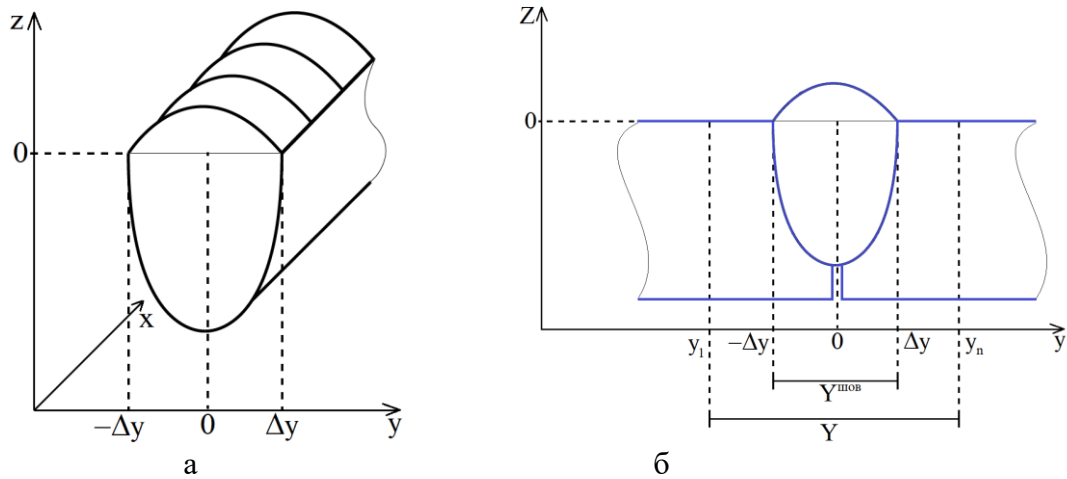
Принципиальный график (а) и поперечное сечение (б) сварного шва изделия, где x – ось длины сварного шва; y – ось ширины сварного шва; z – ось глубины сварного шва
